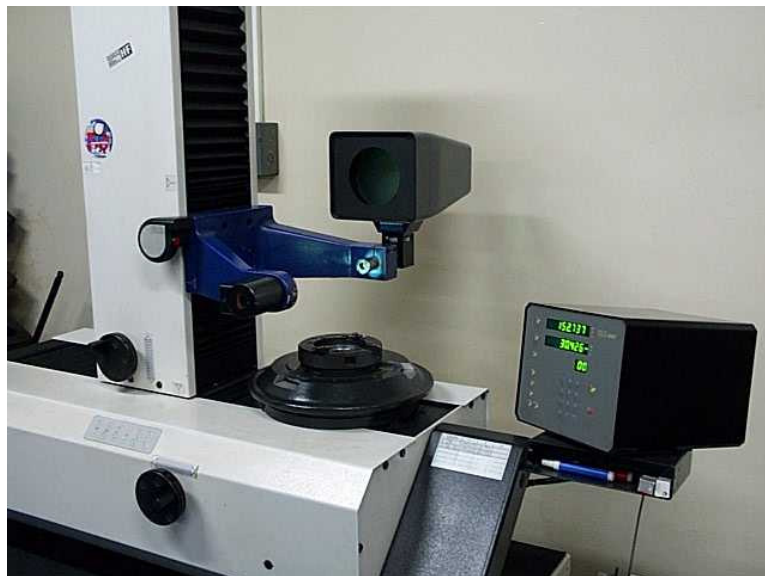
Máquina de medir ferramentas – Presetter (Zoller, 1995)
